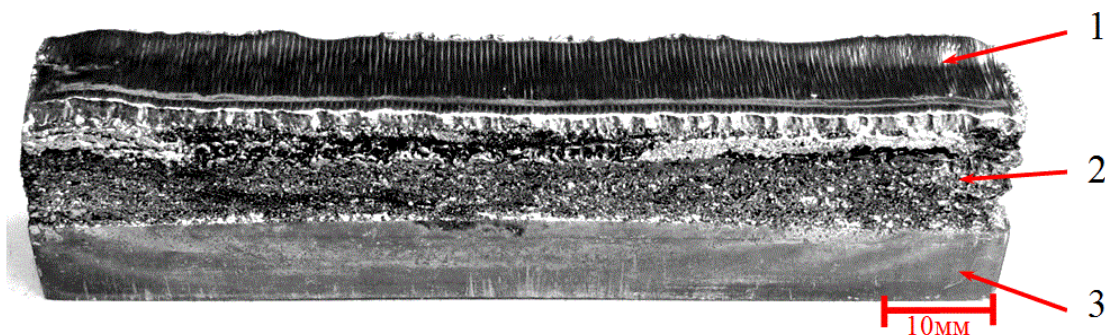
Зразок виробу, виготовлений методом електронно-променевого наплавлення: 1 – верхній шар; 2 – шар наплавленого металу; 3 – підкладка
